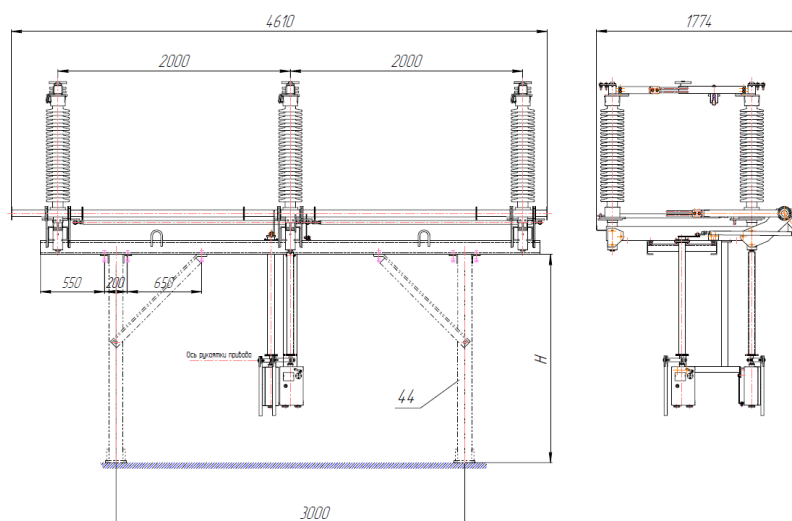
Габаритные размеры РГП-СЭЩ-110/1250 УХЛ 1
